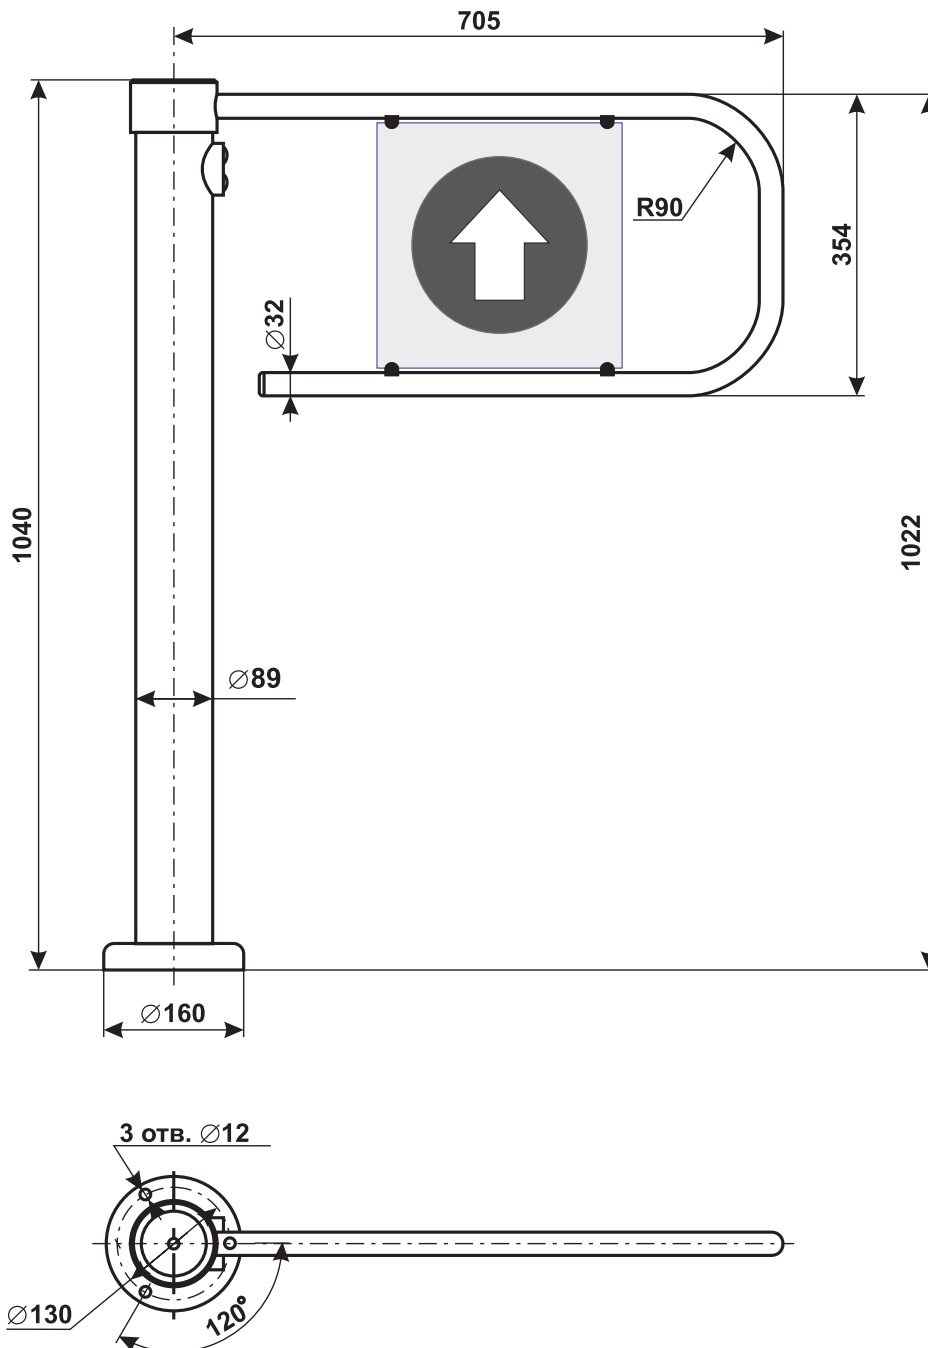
Габаритный чертеж стойки калитки PERCo-WHD-04
